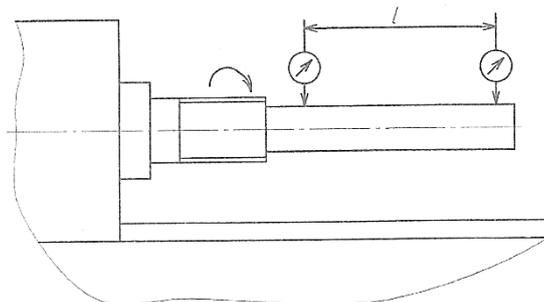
Схема установки индикатора для проверки радиального биения, центрирующей шейки шпинделя
